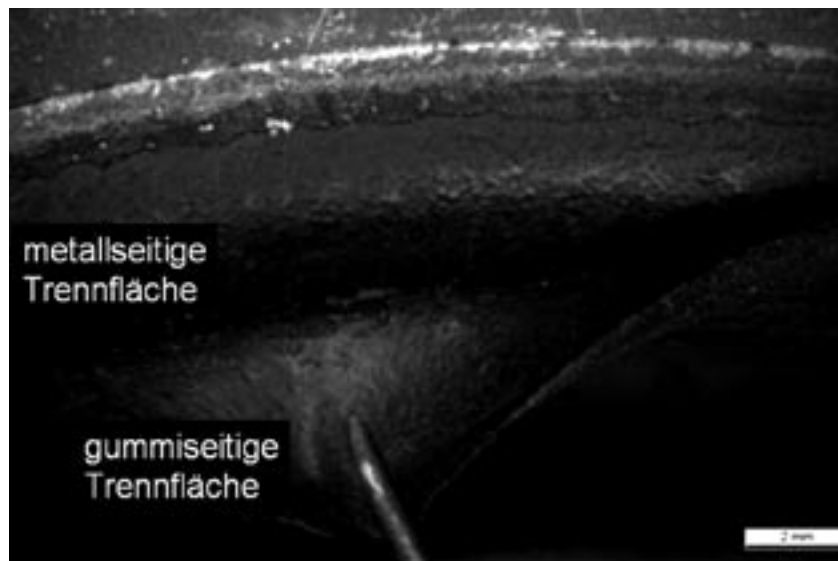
Beispiel für einen Schadensfall an der Grenzschicht zwischen Gummi und Metall bei einem Gummi/Metall-Bauteil. Für die Aufnahme wurde die nicht haftende Gummischicht abgehoben
